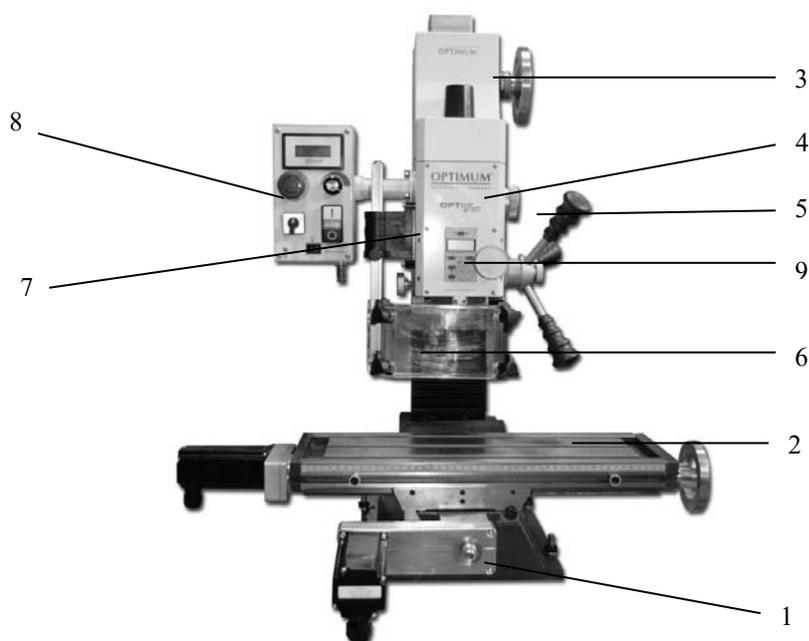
Общий вид фрезерного станка модели Optimum BF20 Vario
